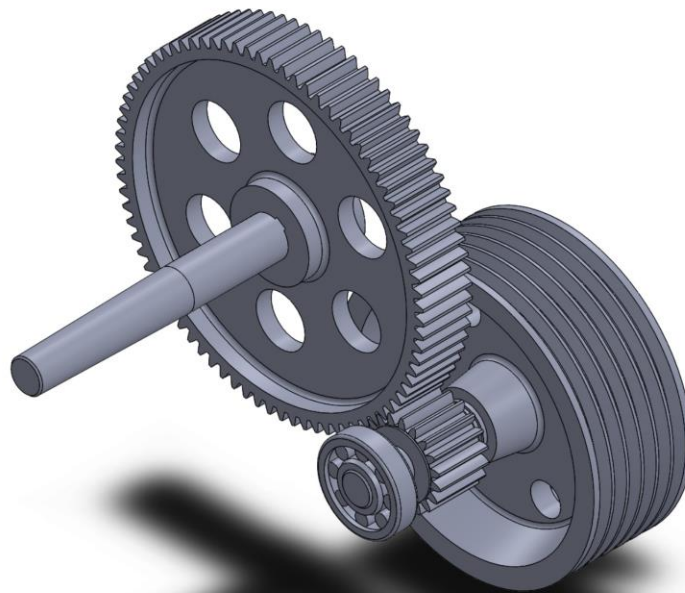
Ізометрія конструкції вал-шестерня
